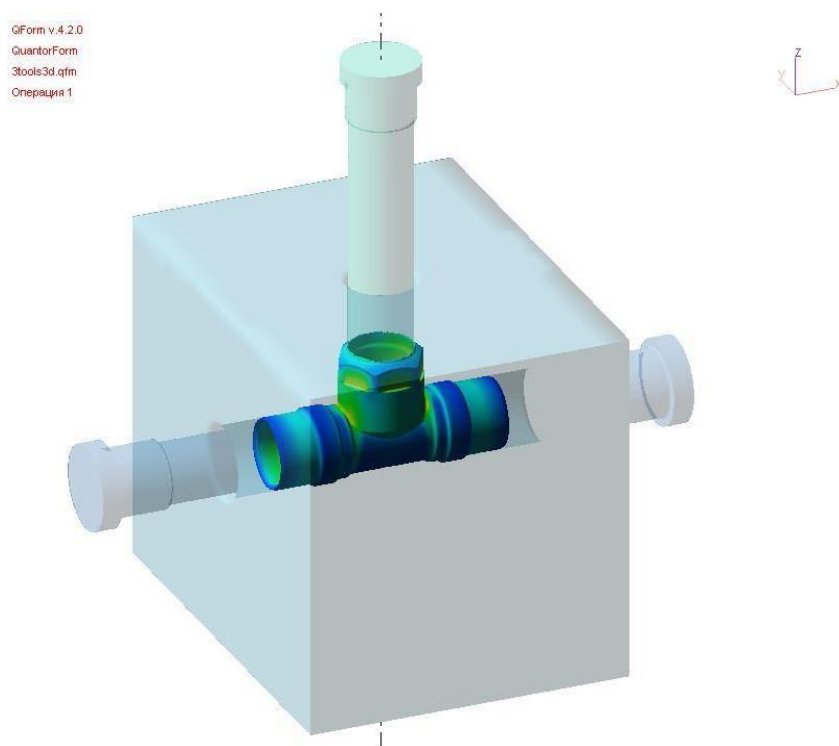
Схема штамповки корпуса трубопроводной арматуры
